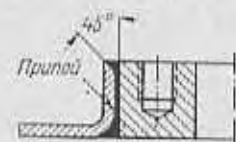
Узел соеди- нения бобышки с корпу- сом аппарата на твердом или мягком припое
